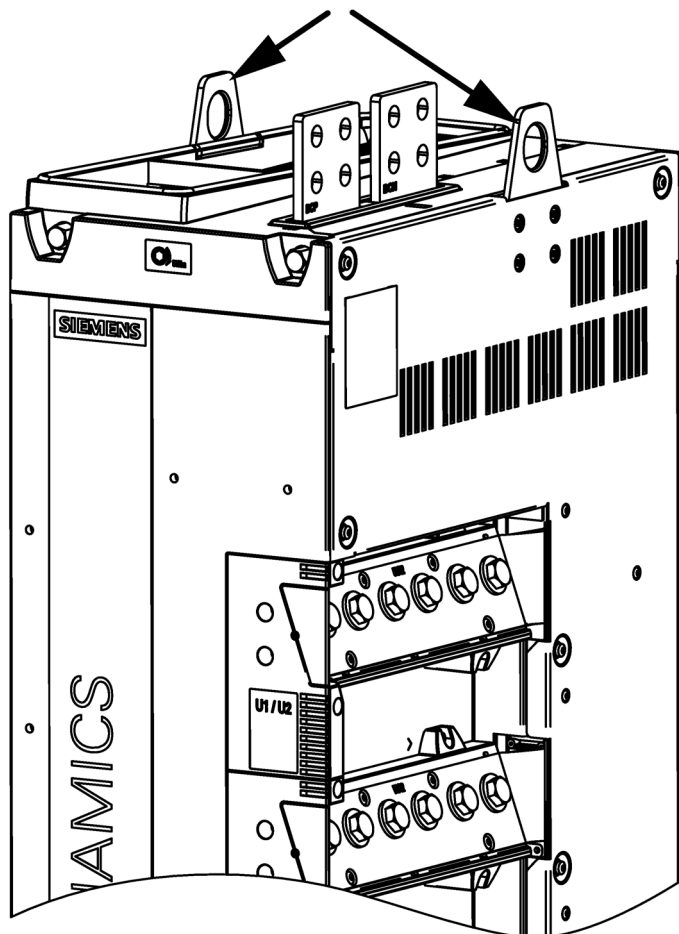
Проушины для крана на модуле двигателя формата «шасси-2» типоразмера FS4
